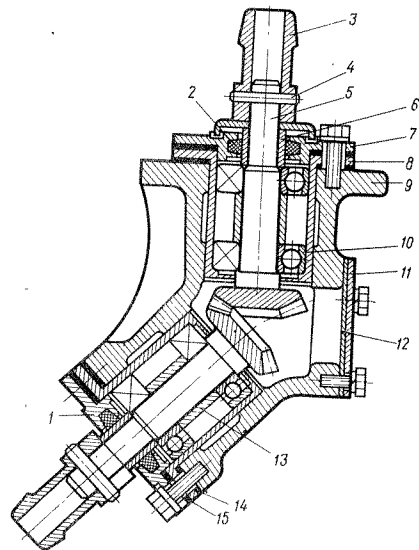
Промежуточный редуктор: 1, 7, 11 — крышки; 2 — уплотнительное кольцо; 3 — наконечник; 4 — штифт; 5 — вал-шестерня; 6, 13 — втулки; 8 — гнездо подшипника; 9 — корпус редуктора; 10 — подшипник; 12, 14, 15 — прокладки
